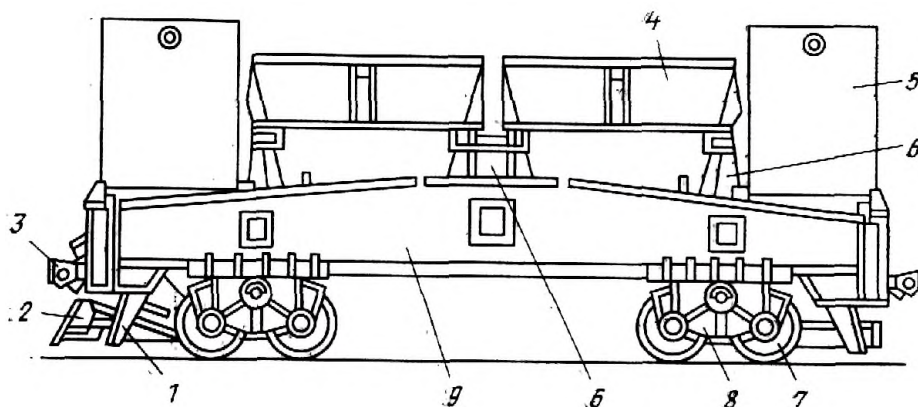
Самоходный шлаковоз с двумя шлаковыми ковшами
